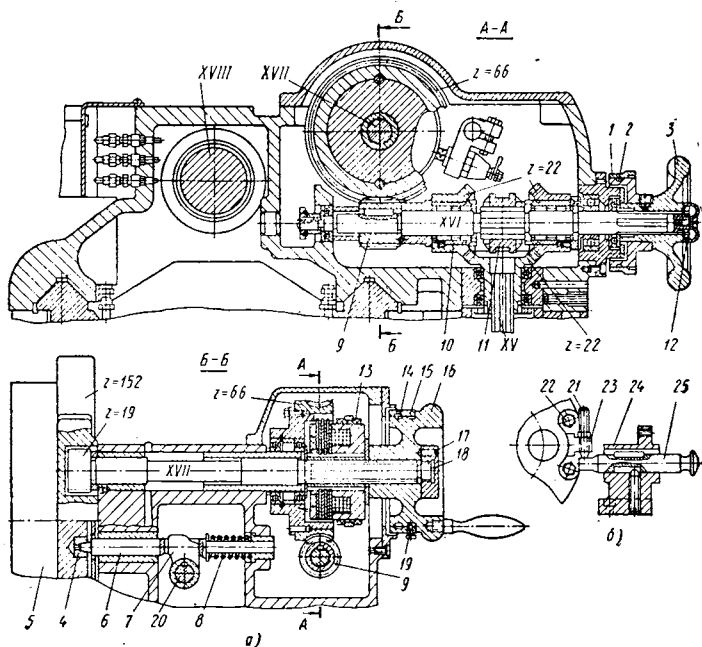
Револьверный суппорт станка 1341 (а) и поперечный упор (б)
